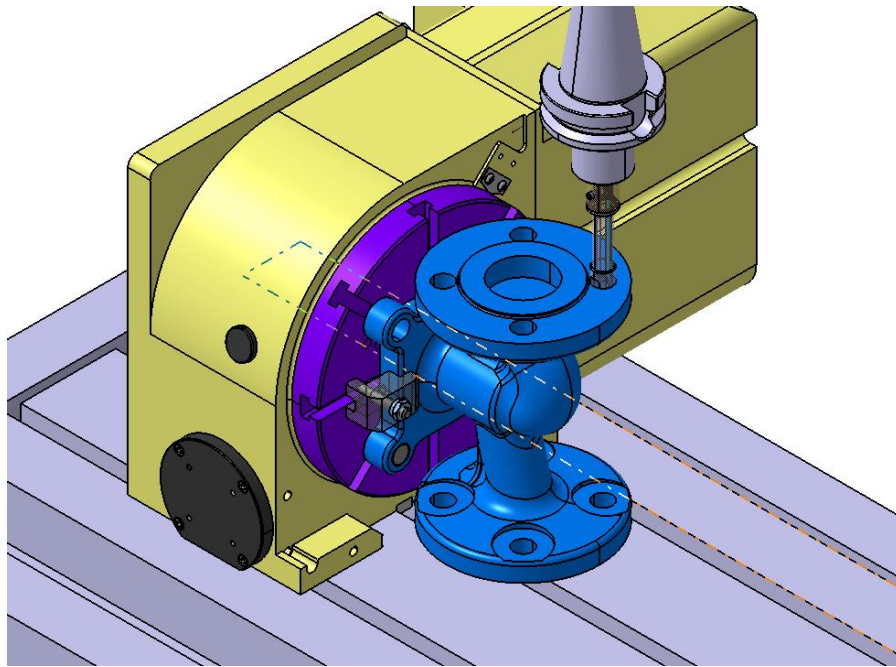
Наладка на свердильно-фрезерну операцію
